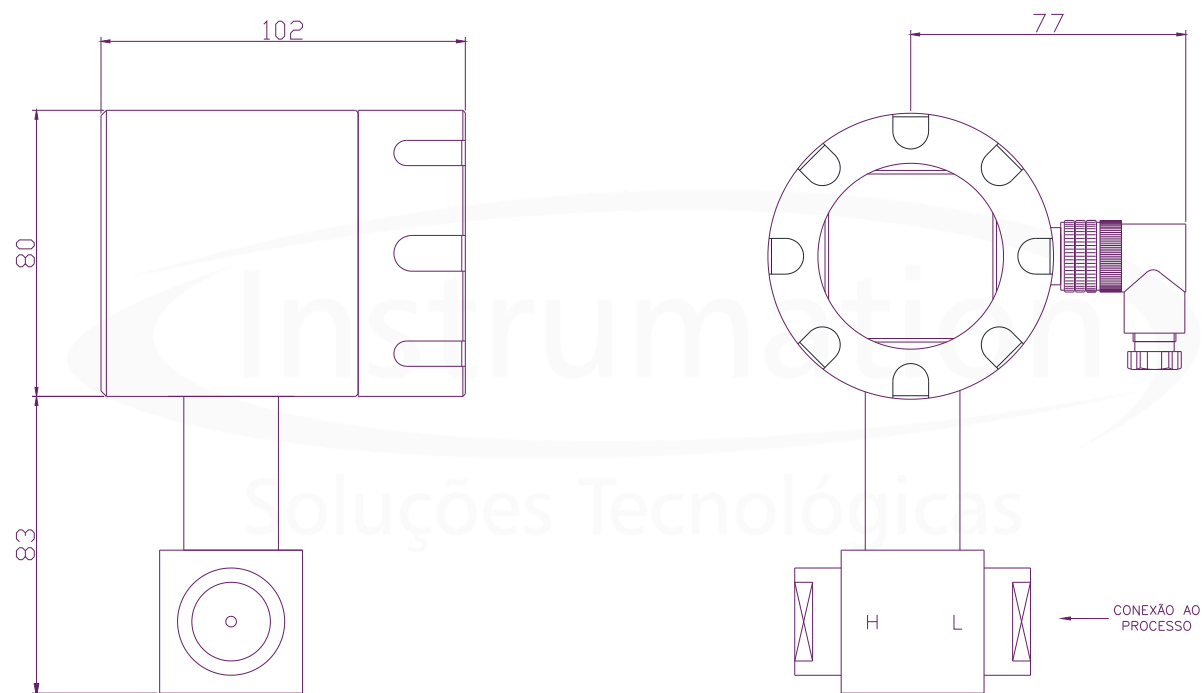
Desenho Dimensional de Montagem - Pressostato Diferencial Digital PDD 1005
